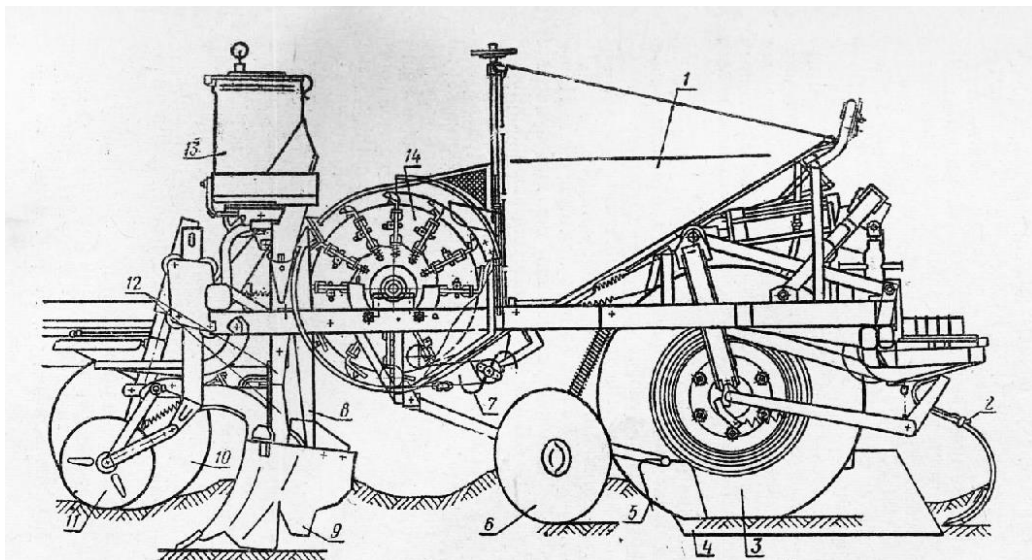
Картофелепосадочная машина СКМ-6: 1 — бункер; 2 — рыхлительная лапа; 3 — ходовое колесо; 4 — стабилизатор; 5 — боронка; 6 — заделывающий диск; 7 — ворошилка; в — отражатель; 10 — сошник; 10 — опорное колесо; 11 — копирующее колесо; 12 — тукопровод; 13 — туковысевающий аппарат; 14 — вычерпывающий аппарат. Для получения устойчивых междурядий при работе на небольших склонах (до 5°) сажалка оборудована стабилизатором, выполненным в виде стальной пластины. Стойками пластина крепится к кронштейнам рамы.
